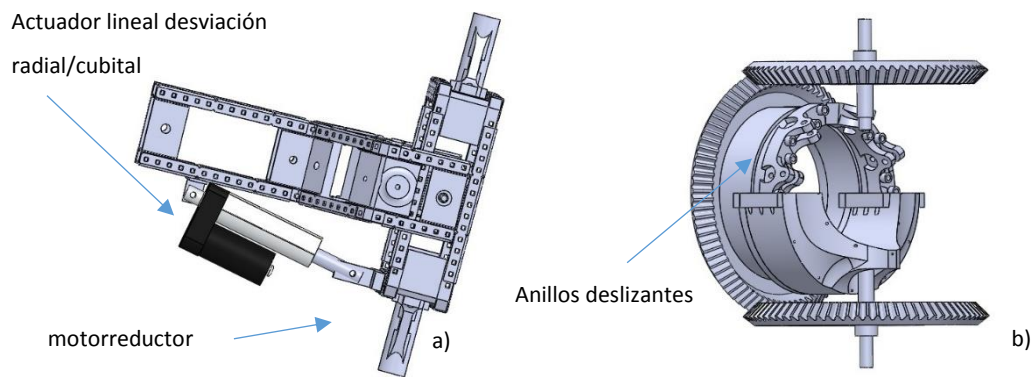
a) Ensamble bastidor y horquilla. b) Ensamble de anillos deslizantes.
